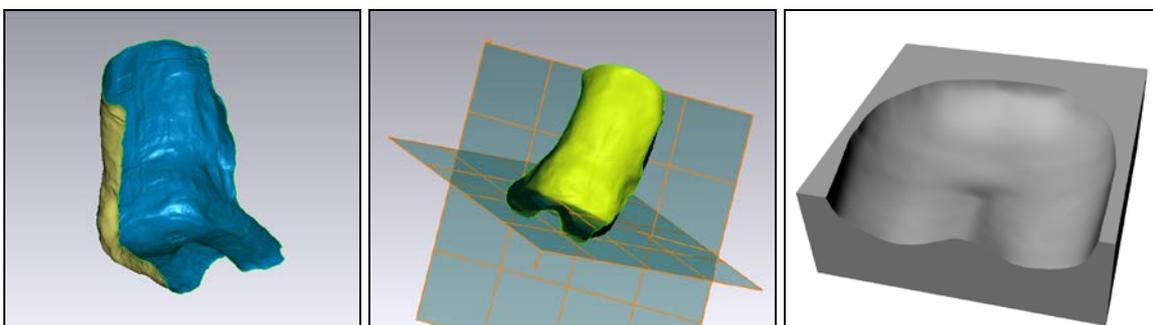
Modelagem CAD/CAM para usinagem da espuma.
